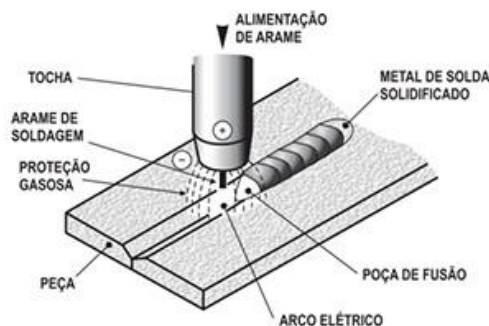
Processo básico de soldagem MIG/MAG (ESAB, 2005).
